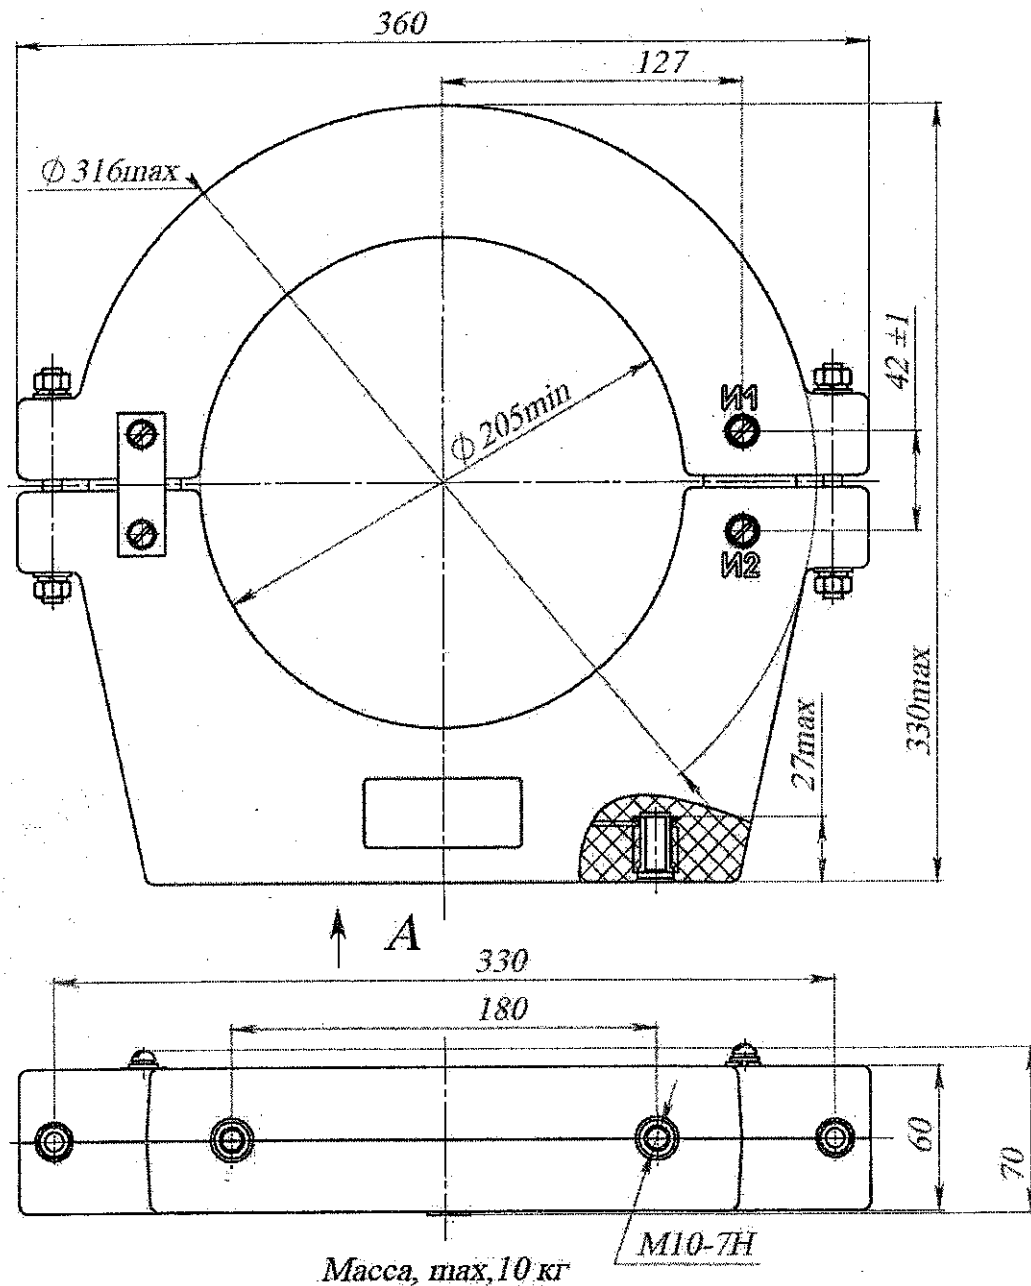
Общий вид и габаритные размеры трансформатора тока ТЗРА-200-470/1
